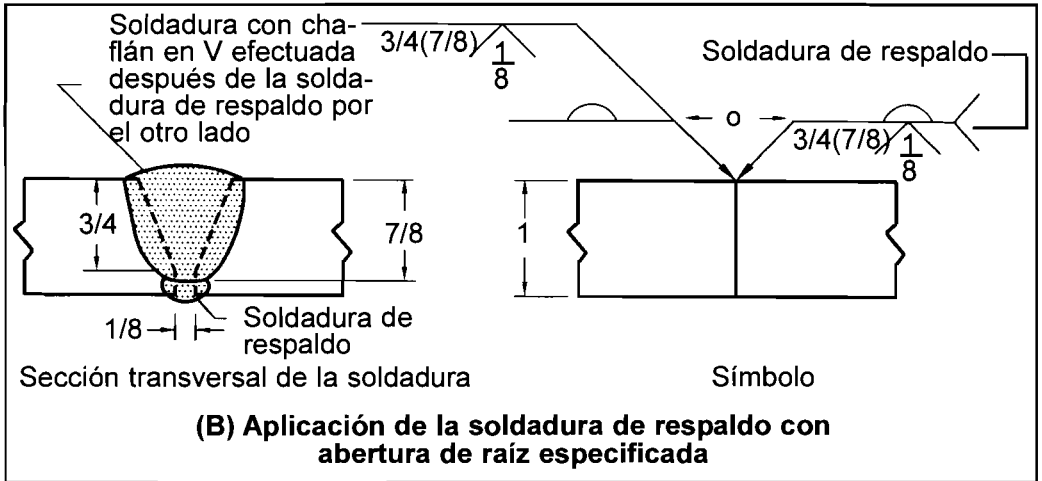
(CONTINUACIÓN): APLICACIONES DEL SÍMBOLO DE SOLDADURA DE REVERSO O RESPALDO
